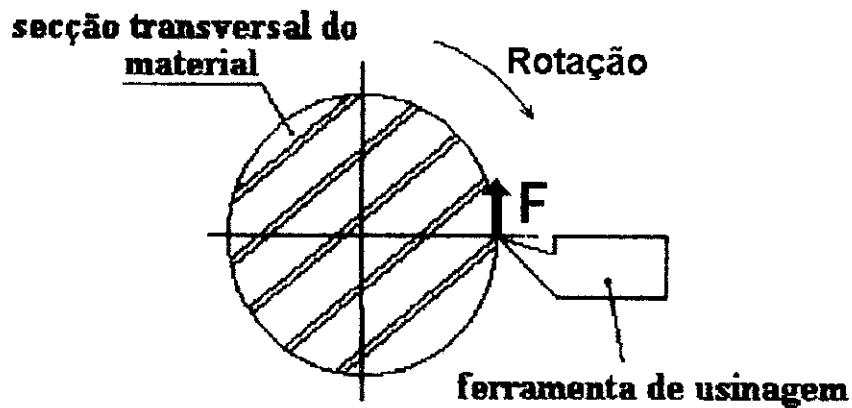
Desenho esquemático de uma ferramenta de usinagem em posição de trabalho numa operação de usinagem denominada torneamento cilíndrico externo.
